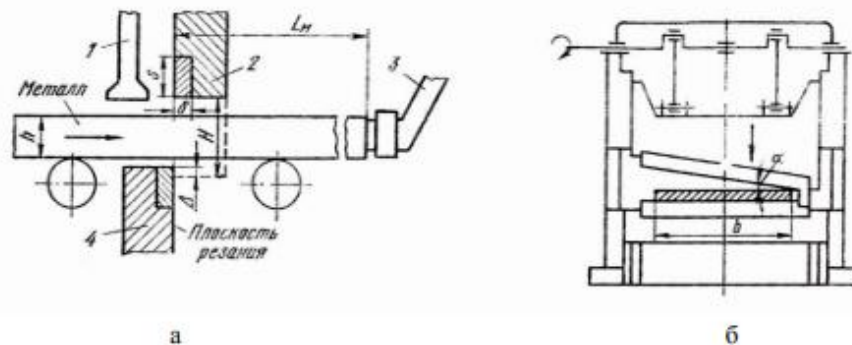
Схема різання металу на ножицях з паралельними (а) і похилими (б) ножами: 1 – притискач, 2 – верхній супорт з ножем, 3 – рухомий упор, 4 – нижній супорт з ножем
